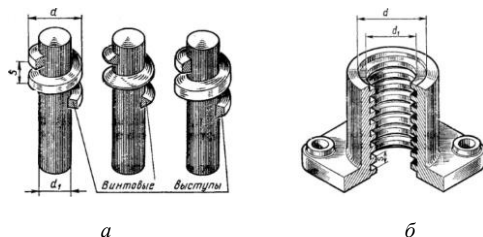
Цилиндрические винты: *a* – наружная резьба; *б* – внутренняя резьба; *d* – внешний диаметр резьбы; *d*<sub>1</sub> – внутренний диаметр резьбы; *S* – шаг резьбы
